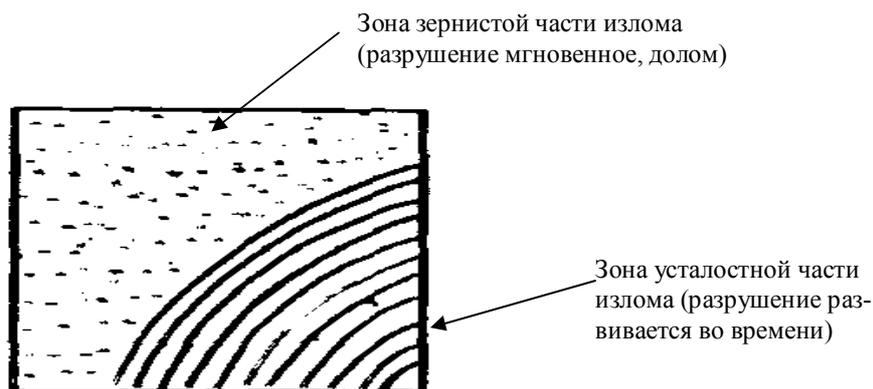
Схема усталостного излома, прошедшего по шейке коленчатого вала
